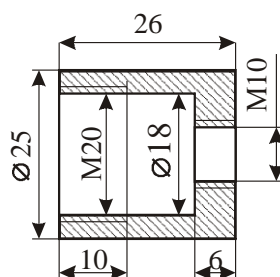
Эскиз крышки капсулы с отверстием для запрессовки оболочки термопары
